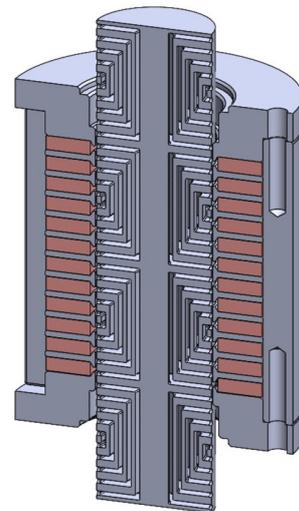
Rendering in sezione di due poli del motore tubolare sincrono a riluttanza con movente in additive manufacturing
